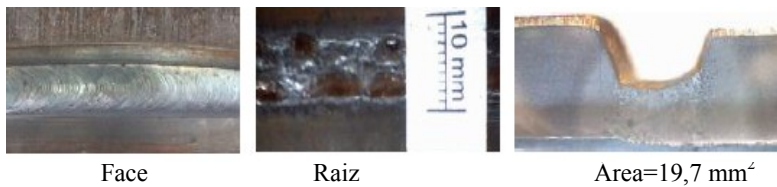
Solda 5G, cordão C, com pulsado de 1 Hz.
